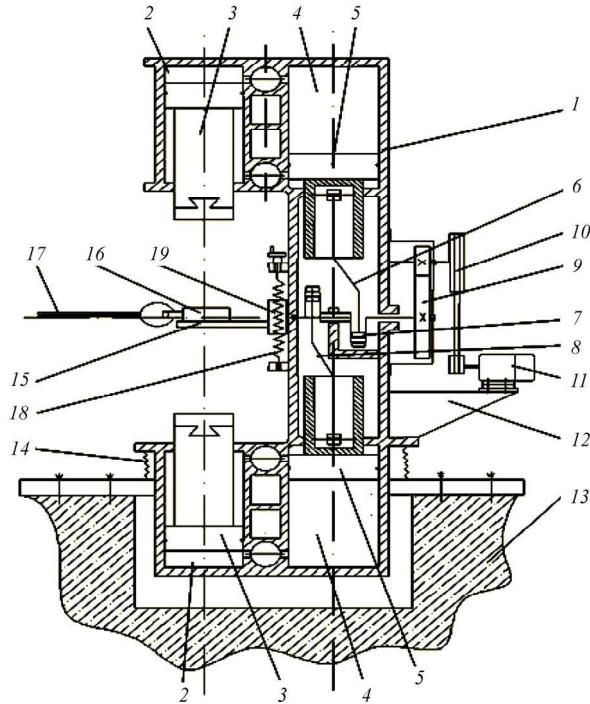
Приводной бесшаботный пневматический молот со встречным ударом баб: 1 – станина; 2 – рабочий цилиндр; 3 – баба; 4 – компрессорный цилиндр; 5 – поршень; 6 – шатун; 7 – коленчатый вал; 8 – шатун; 9 – редуктор; 10 – клиновременная передача; 11 – электродвигатель; 12 – основание; 13 – фундамент; 14 – амортизаторы; 15 – упругодеформируемая площадка; 16 – заготовка; 17 – клемши; 18 – винт; 19 – гайка
